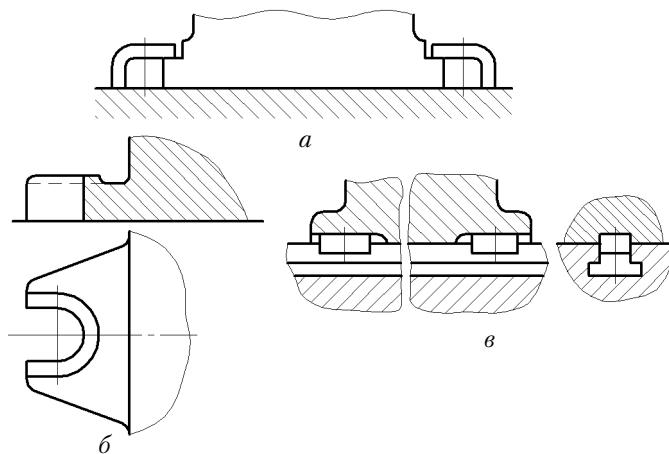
Варианты базирования и закрепления корпуса приспособления на столе станка
